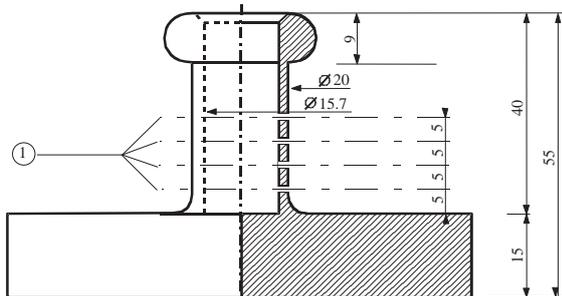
Cylindre creux en bronze, fermé d'un côté ; Plan et coupe verticale, dimensions en mm
